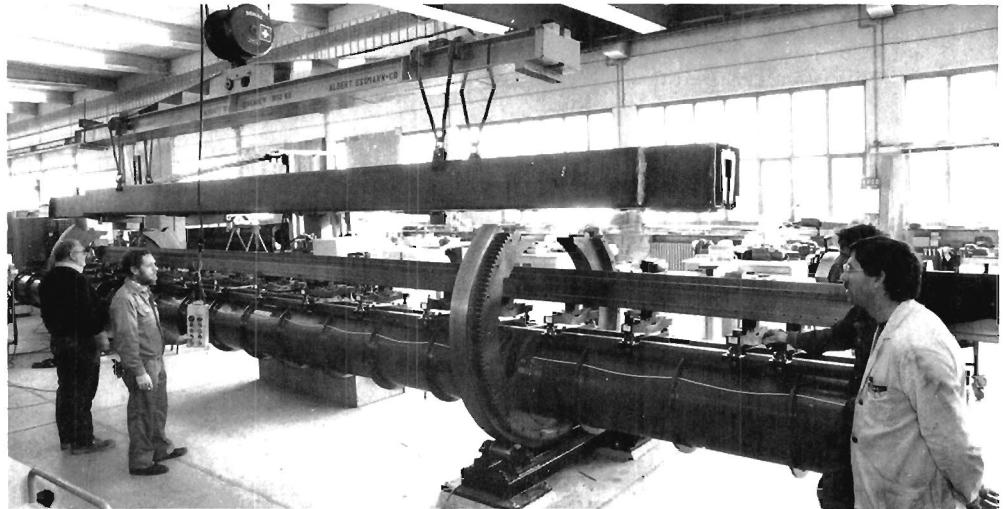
Ein Elektronenring-Dipol wird aus der Stapelmaschine herausgehoben. (38591/22)
